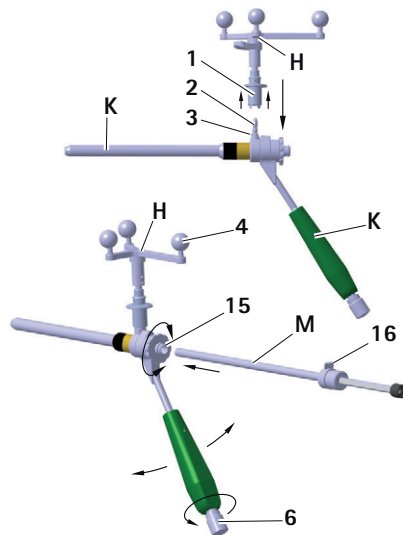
Монтаж звездчатого опорного блока Aescular на направляющей втулке S⁴C; установка направителя сверла S⁴C
